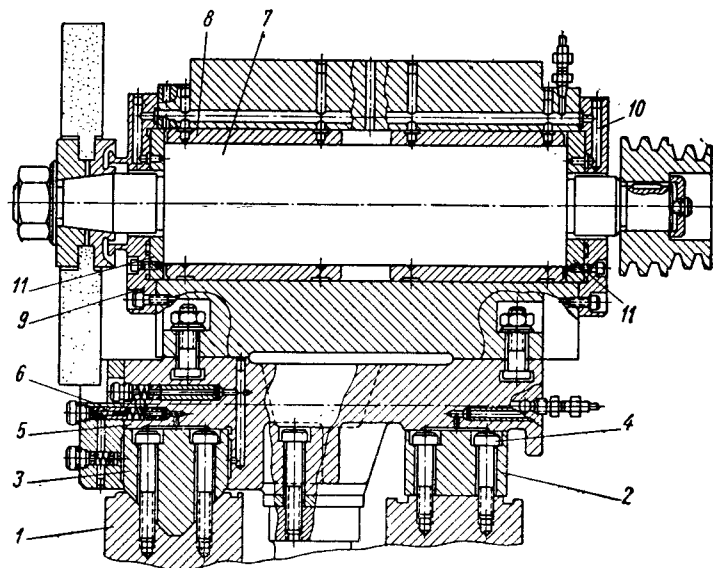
Бабка шлифовального круга на аэростатических направляющих:
